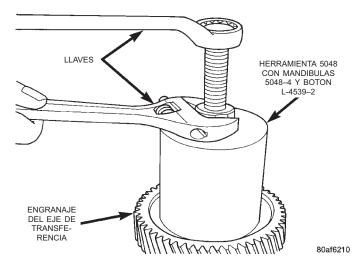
Desmontaje del cono de cojinete del engranaje de transferencia
